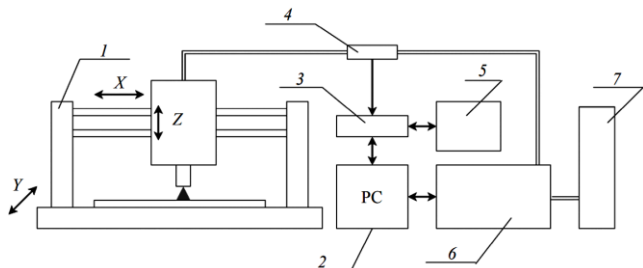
Экспериментальный стенд по 3D-наплавке на базе станка с ЧПУ: 1 – 3-координатный станок с ЧПУ портального типа; 2 – ПК; 3 – АЦП/ЦАП; 4 – датчики силы тока и напряжения; 5 – система ЧПУ; 6 – сварочный полуавтомат; 7 – баллоны с защитным газом
